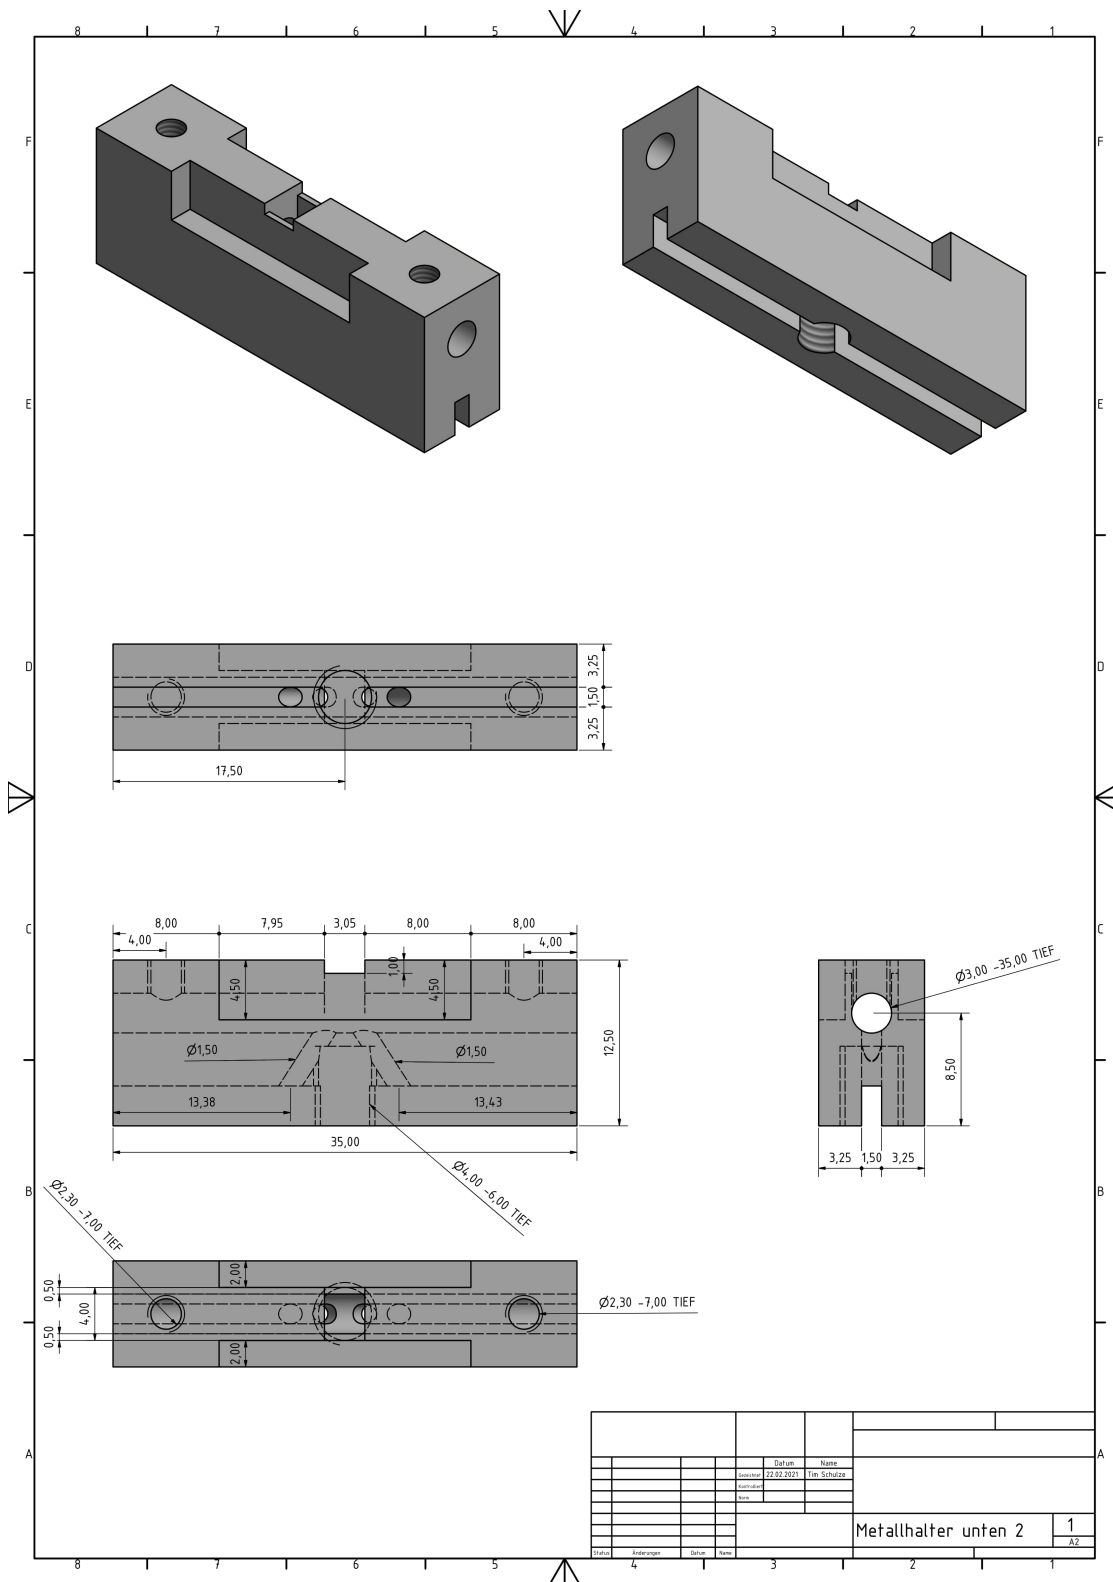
Technische Zeichnung des unteren gefrästen Metallhalters für den aktuierbaren Wellenleiter
